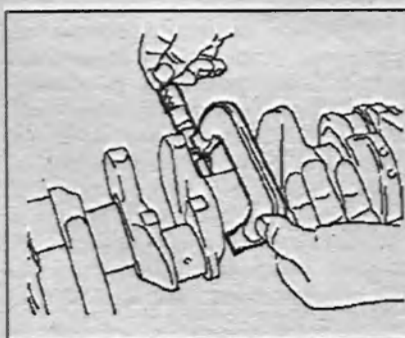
Измерение диаметра шейки коренного подшипника.
